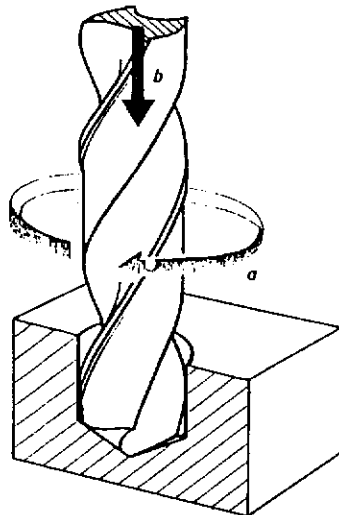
,1. Movimiento al taladrar con la máquina de taladrar. a) Movimiento de corte principal; b) movimiento de avance.
